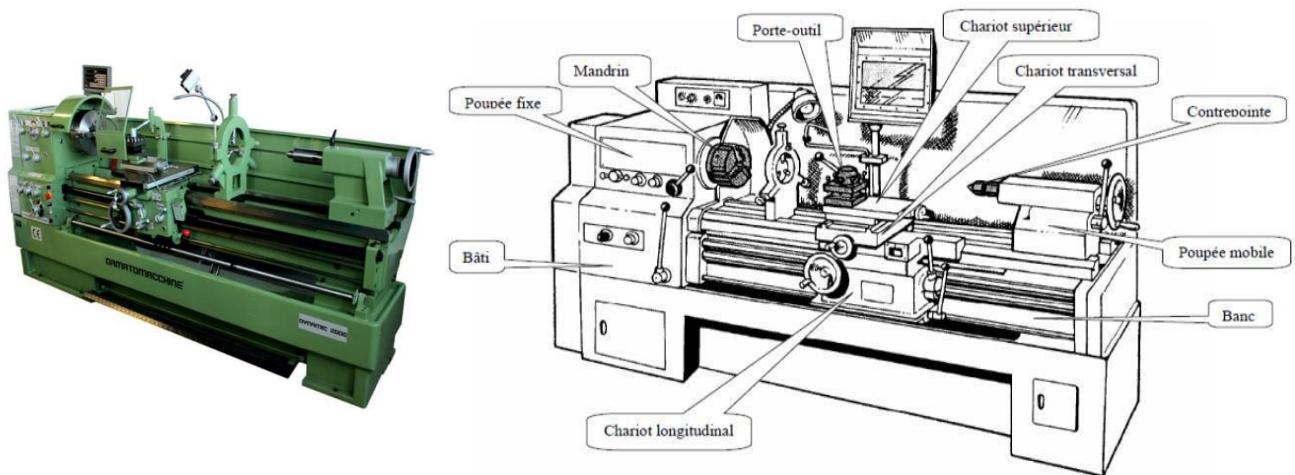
Vue d'ensemble et composants d'un tour parallèle.
